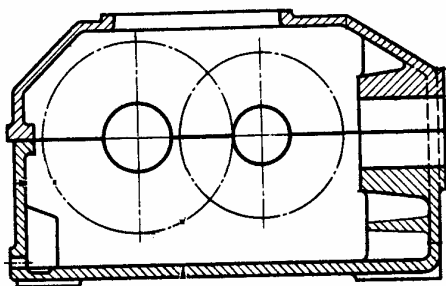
Корпус с разъемом в плоскости осей валов коническо-цилиндрического редуктора
